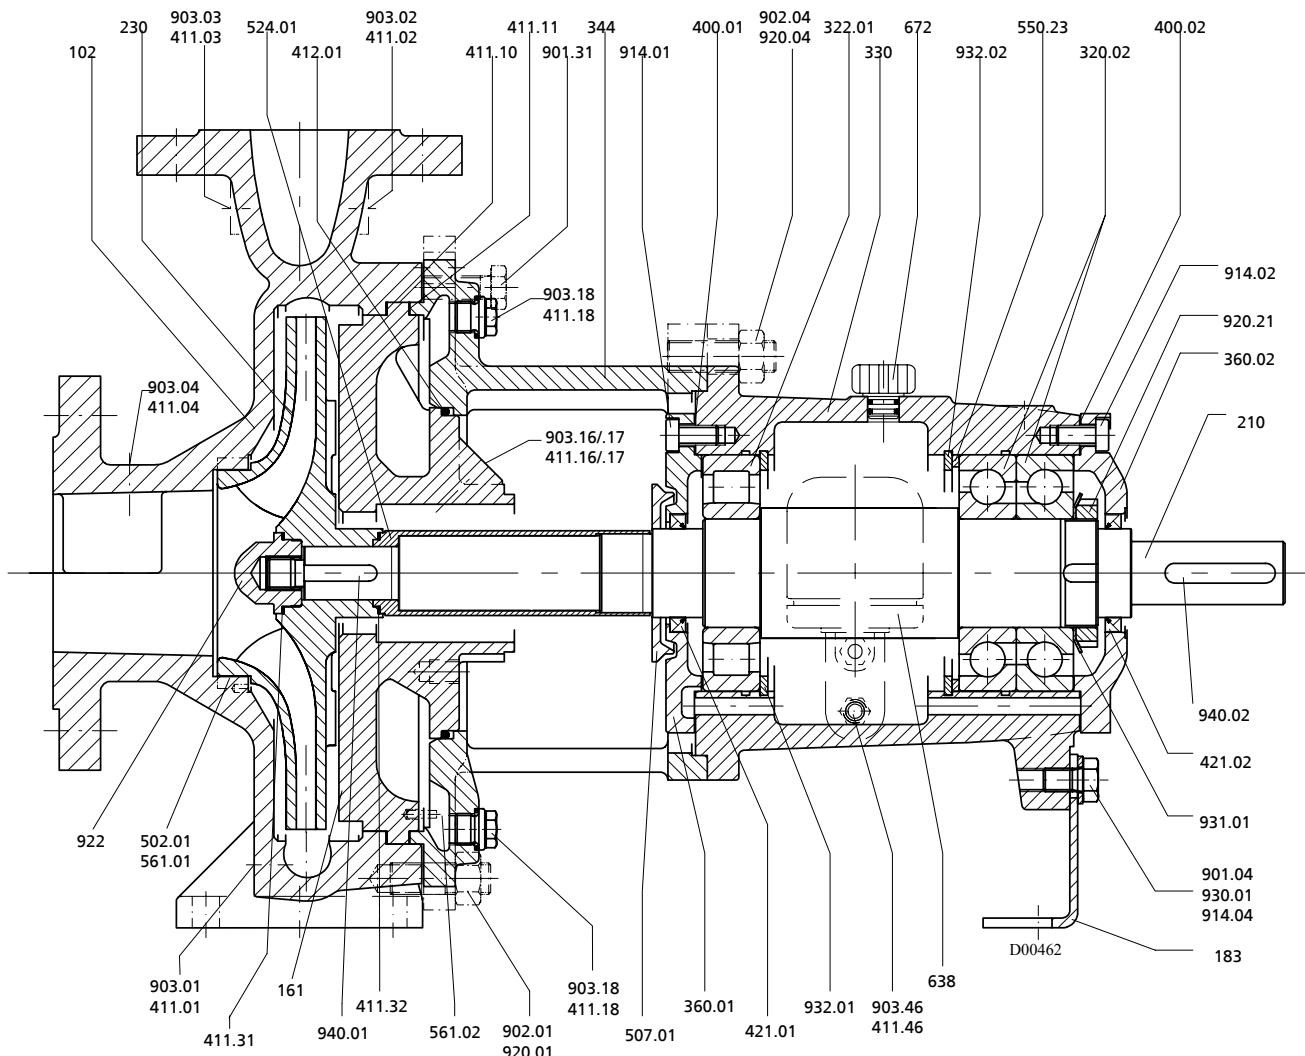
Общий чертеж стандартного исполнения (с масляной смазкой)
